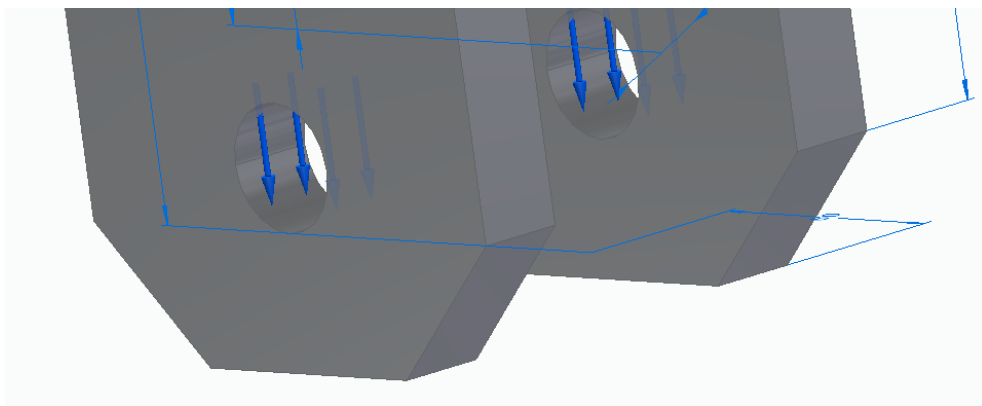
Detalle de la adición de las restricciones y cargas en la pieza
